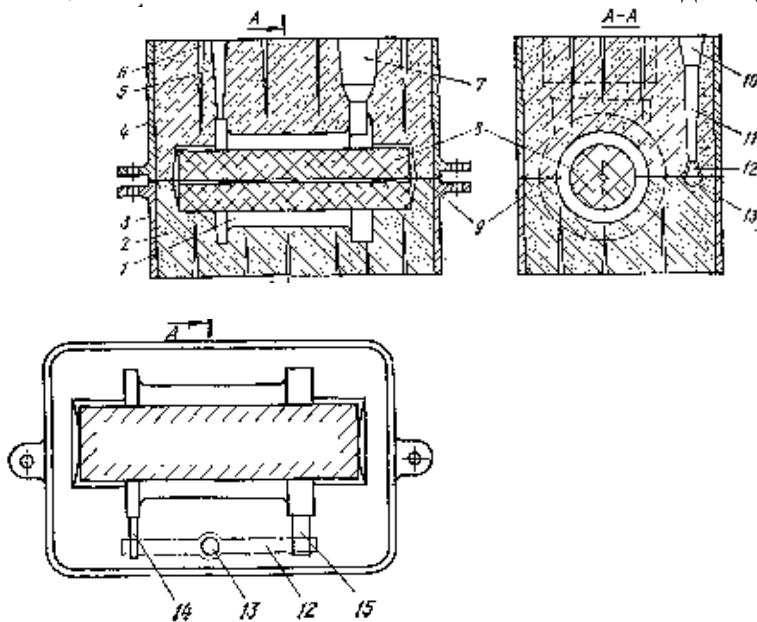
Эскиз литейной формы: 1 — собственно полость формы; 2 — формовочная смесь; 3 — опока нижней полуформы; 4 — опока верхней полуформы; 5 — выпор; 6 — вентиляционный канал; 7 — прибыль; 8 — стержень; 9 — плоскость разъёма формы (лад); 10 — литниковая воронка; 11 — стояк; 12 — шлакоуловитель; 13 — зумпф; 14, 15 — питатели.
